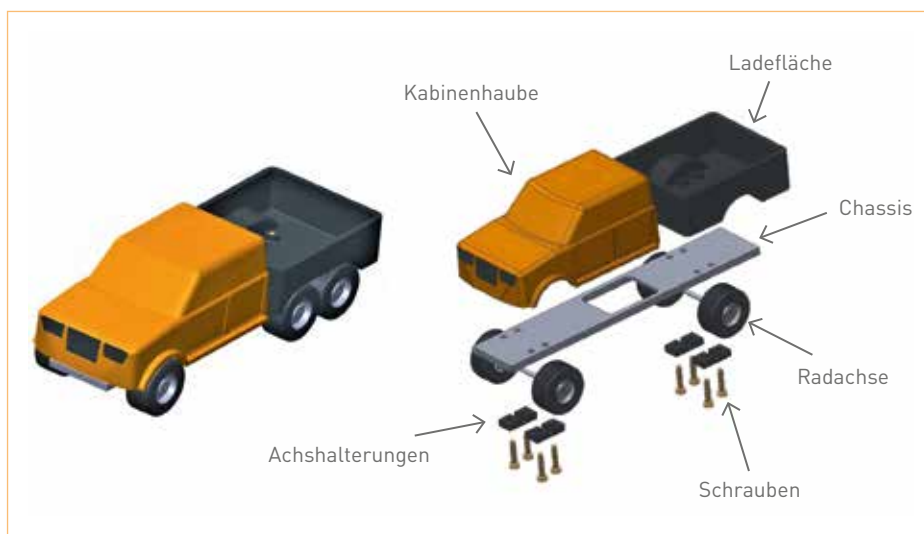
3D-CAD Modell des Modell-Pick-Up-Trucks in der Variante mit drei Achsen (links) sowie als Explosionsansicht mit zwei Achsen (rechts)
